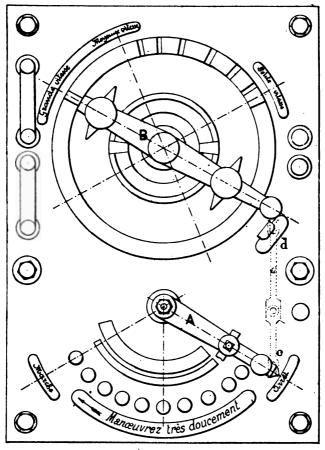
Tableau de couplage des ventilateurs des machines et chausseries (léna); vue extérieure.
